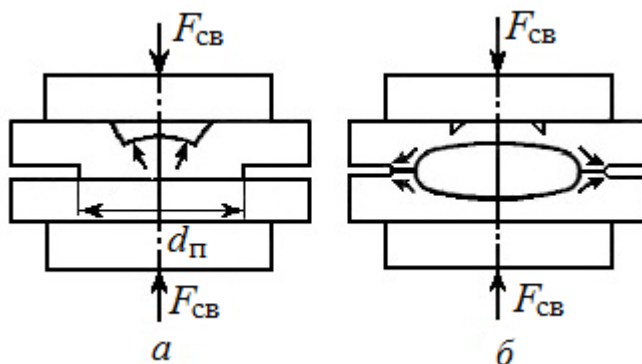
Пластическая деформация металла при рельефной сварке:
